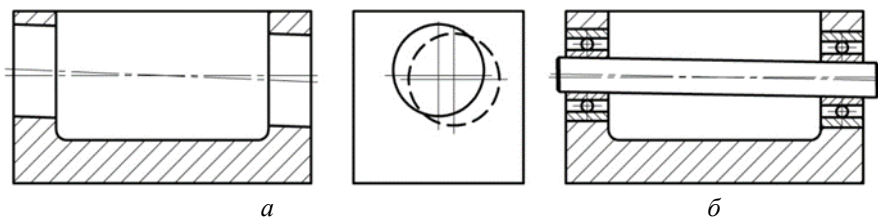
Поворот осі вала щодо основних баз корпусу:
